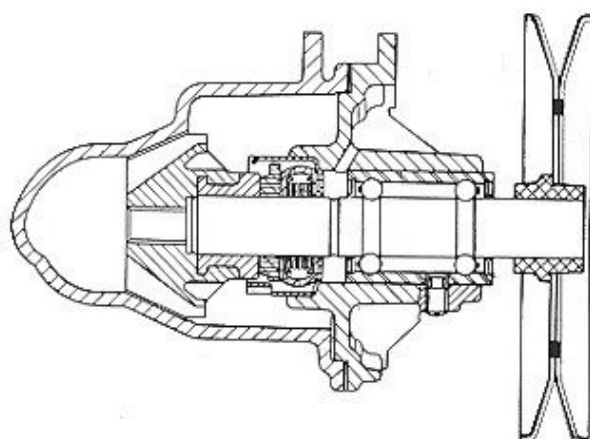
Längsschnitt durch die Kühlwasserpumpe.
